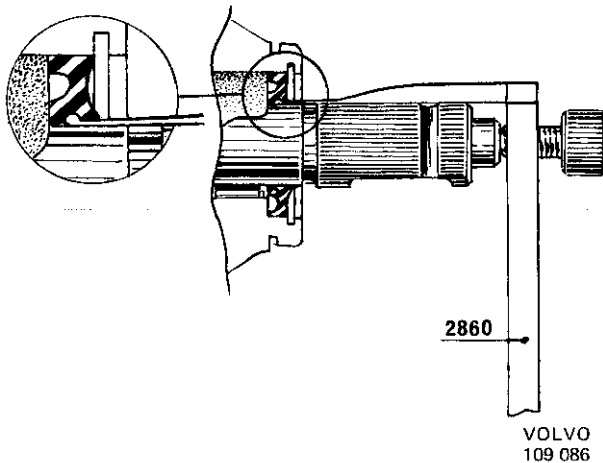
Ausbau des Wellendichtringes, Schneckenwelle
